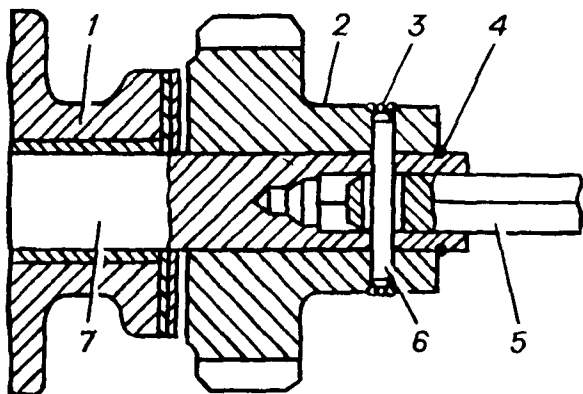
Привод датчика-распределителя зажигания и масляного насоса: 1 – корпус; 2 – шестерня; 3 – пружинное кольцо; 4 – стопорное кольцо; 5 – валик привода масляного насоса; 6 – штифт; 7 – валик привода датчика-распределителя зажигания
